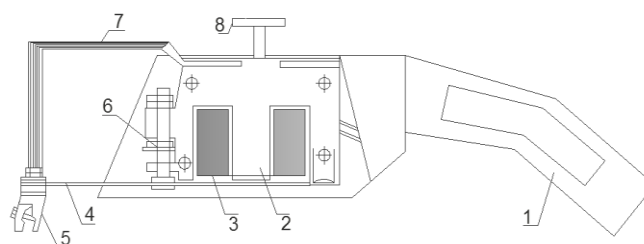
б - Электромагнитный вибратор: 1 - корпус; 2 - сердечник; 3 - катушка; 4 - ярлык; 5 - электроподдержатель; 6 - гайка регулировочная; 7 - токопровод; 8 - винт регулировочный
